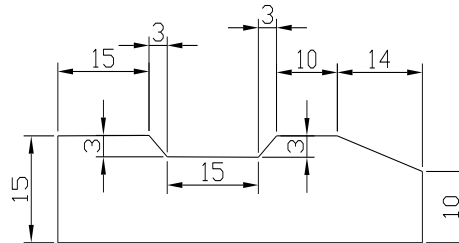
Croquis y dimensiones de la pieza diseñada en solidworks
